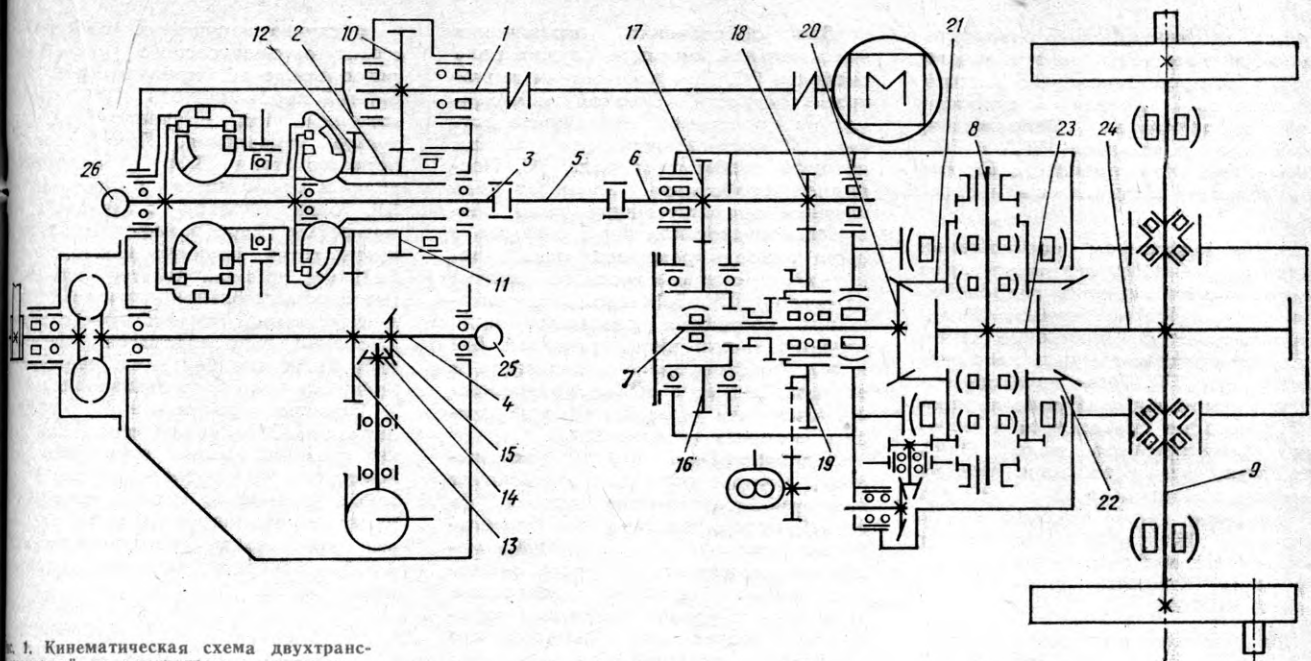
Кинематическая схема двухтрансформаторной гидропередачи с реверсом
